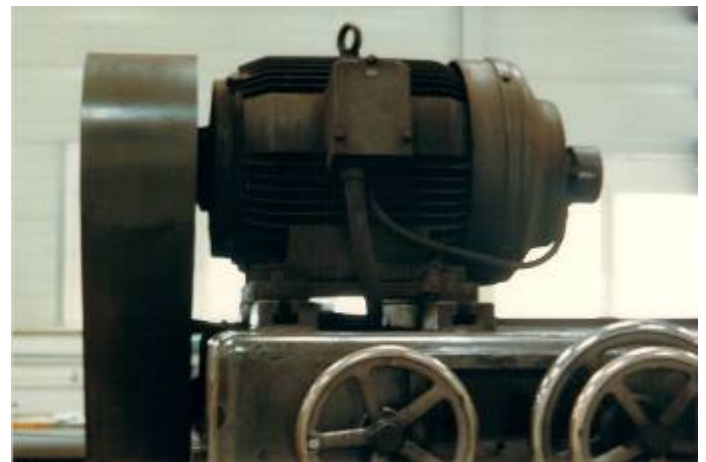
Die alte Maschine hatte die Hauptmotoren auf dem Spindelstock befestigt. WU4770
